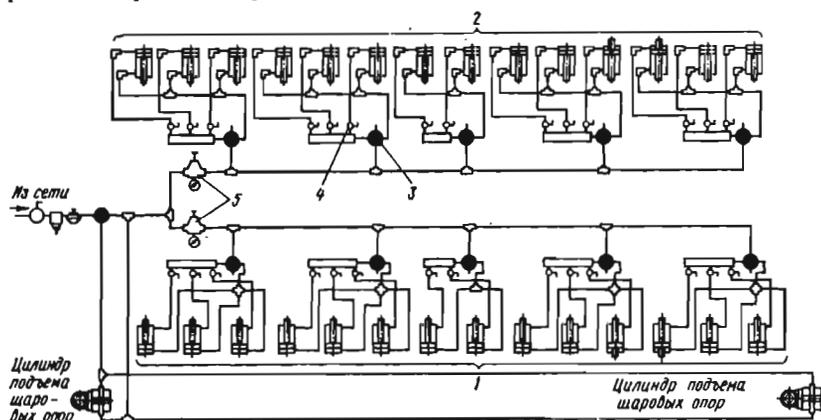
Пневматическая схема станка ФОЛ-2М
